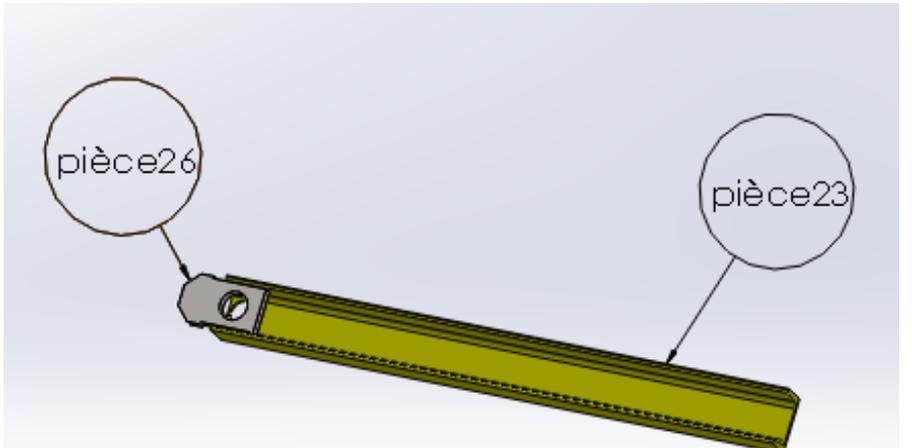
Repérage joint de soudure panneau n°4
